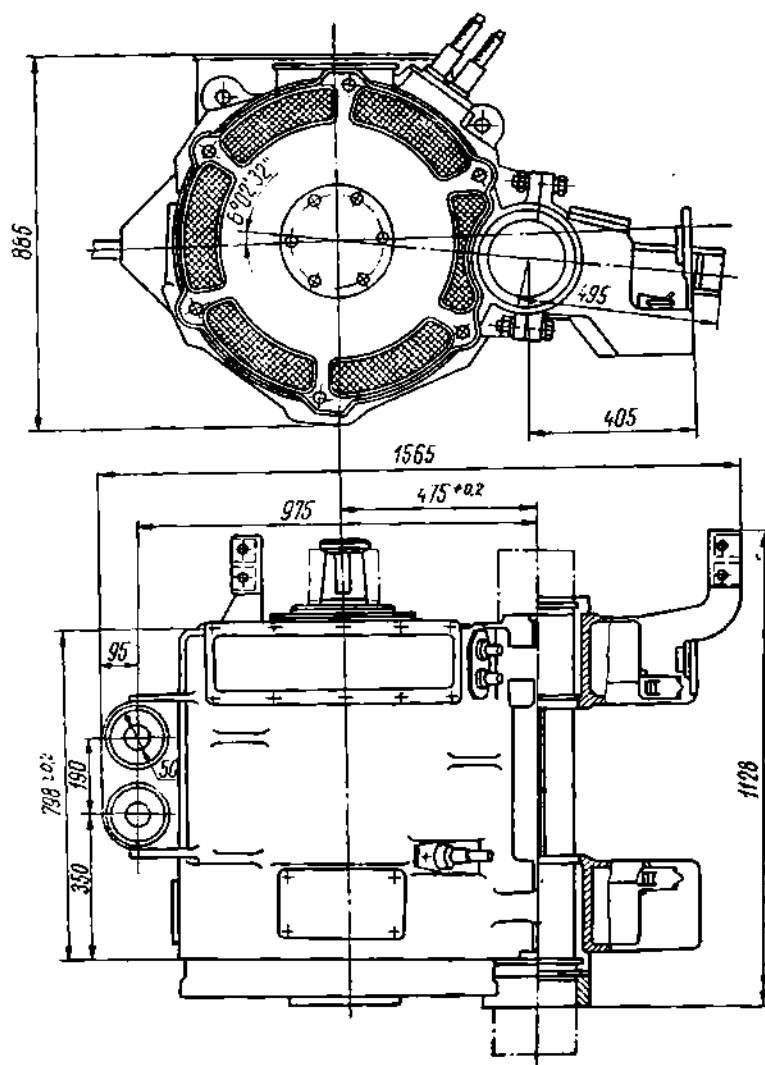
Motor tip GDTM 533 F. Dimensiuni de montaj.
